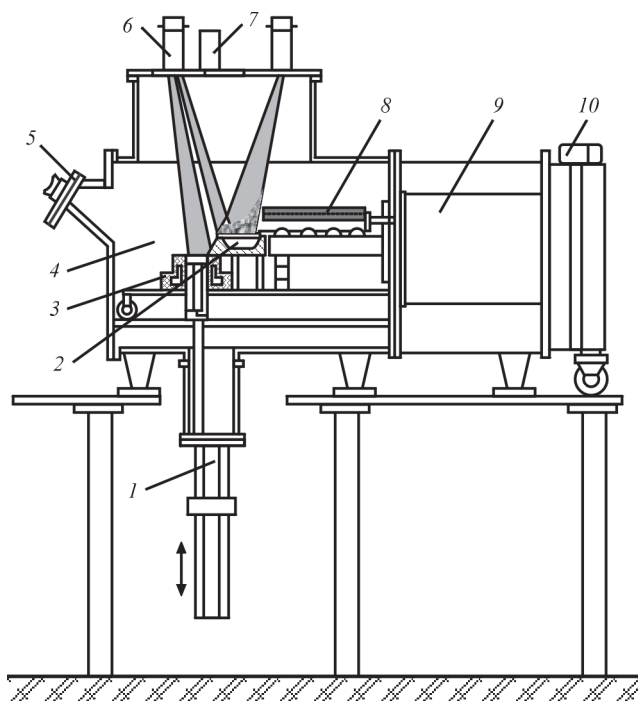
Схема електронно-променевої установки УЕ-208М: 1 — механізм витягування зливка; 2 — проміжна ємність; 3 — кристалізатор; 4 — камера плавки; 5 — оглядова система; 6 — електронно-променеві гармати; 7 — водяний реостат; 8 — витратна заготовка; 9 — камера заготовки; 10 — механізм подачі заготовки
